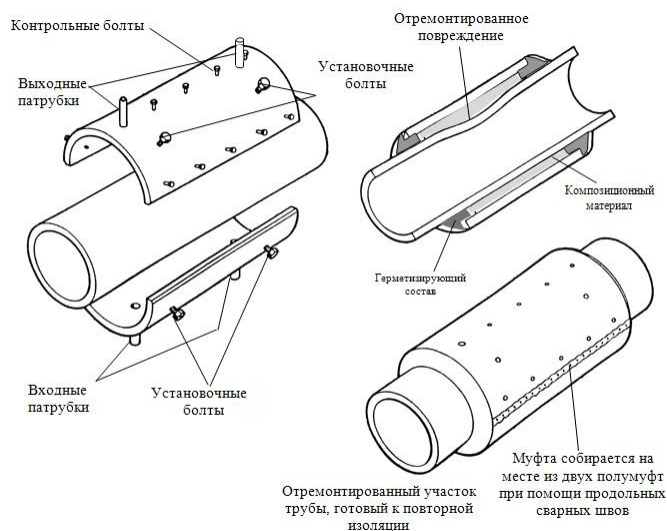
Ремонтная муфта П1 со сварным соединением полумуфт
